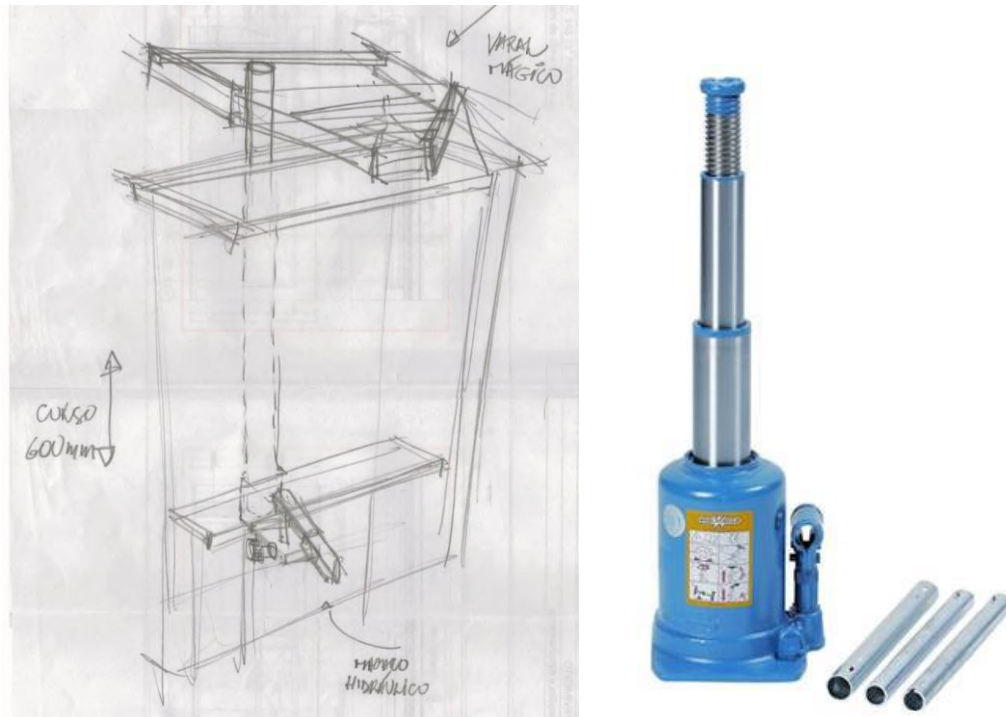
Fase 06 - Esboço sistema de elevação hidráulico
